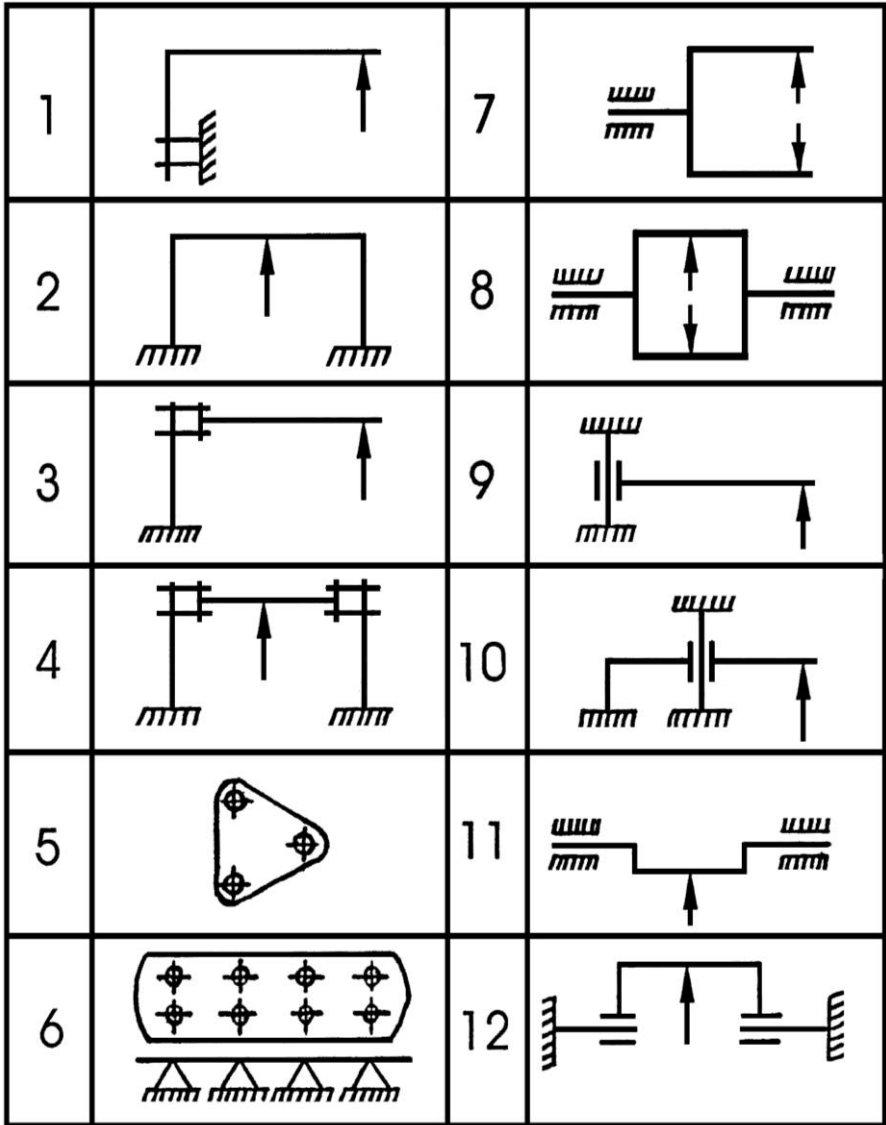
Розрахункові схеми траверс формувальних машин
